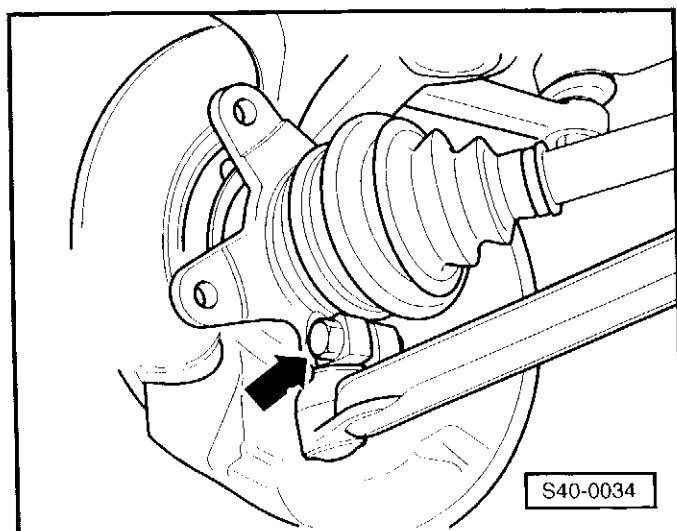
Разборка соединения между рычагом передней подвески и крышкой подшипника ступицы колеса
